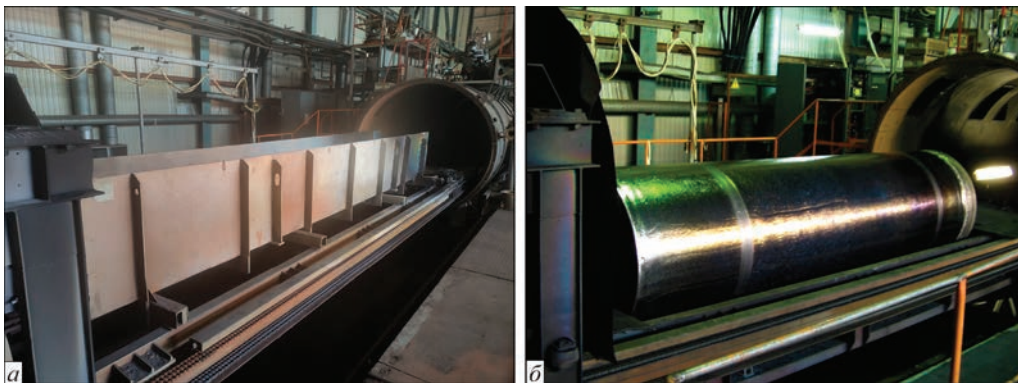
Камера заготовки/опалвлення: а — з завантаженим коробом для виплавки зливка; б — з завантаженим зливком після опалвлення поверхні
